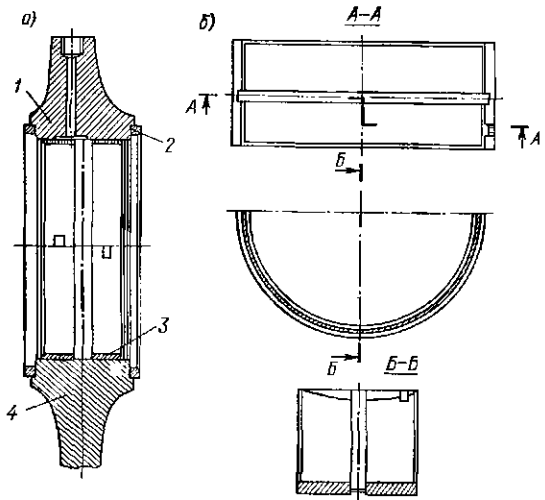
Конструкция опорного подшипника с тонкостенным вкладышем:
